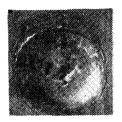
Внешний вид соединения, выполненного дуговой точечной сваркой с принудительными сквозным проплавлением и формованием
